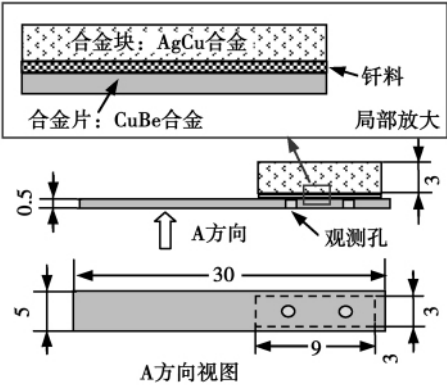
Ag/Cu 连接试验样件结构示意图 (mm)
